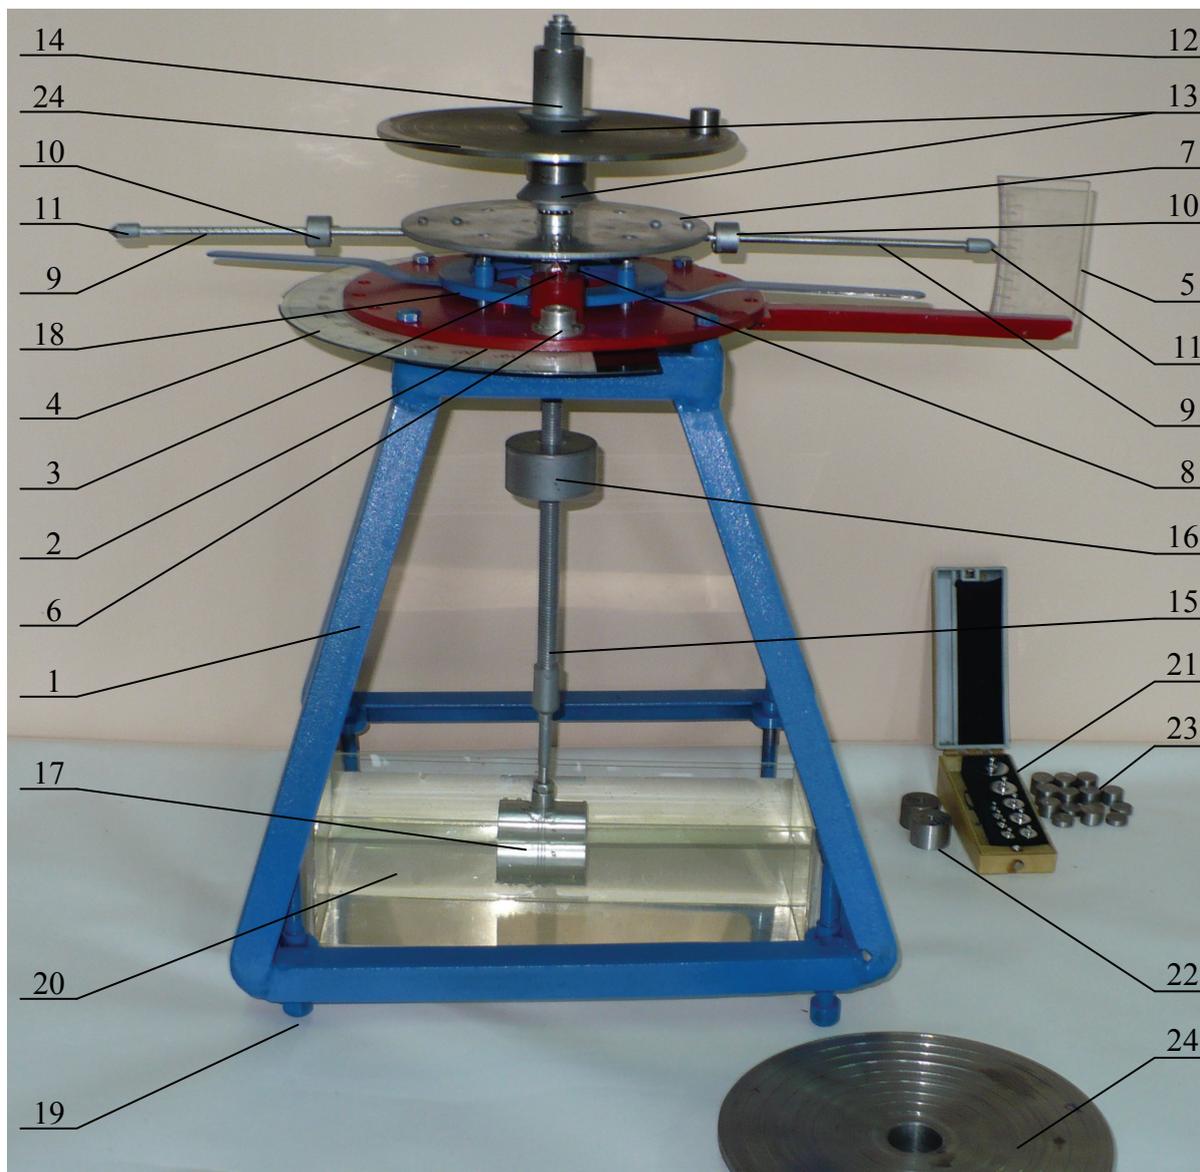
Стенд для статической балансировки вращающихся деталей: 1 – рама; 2 – плита; 3 – призма; 4 – шкала азимута; 5 – шкала момента; 6 – круговой уровень; 7 – фланец; 8 – седло; 9 – стержень; 10 – подвижные грузы; 11 – стрелки-ограничители; 12 – поворотный механизм; 13 – конусные втулки; 14 – гайка; 15 – винт; 16 – груз; 17 – демпфер; 18 – механизм подъема; 19 – винтовая опора; 20 – емкость с демпфирующей жидкостью; 21 – разновесы (1–100 г); 22 – дополнительные подвижные грузы; 23 – набор балансировочных грузов; 24 – балансируемые изделия
